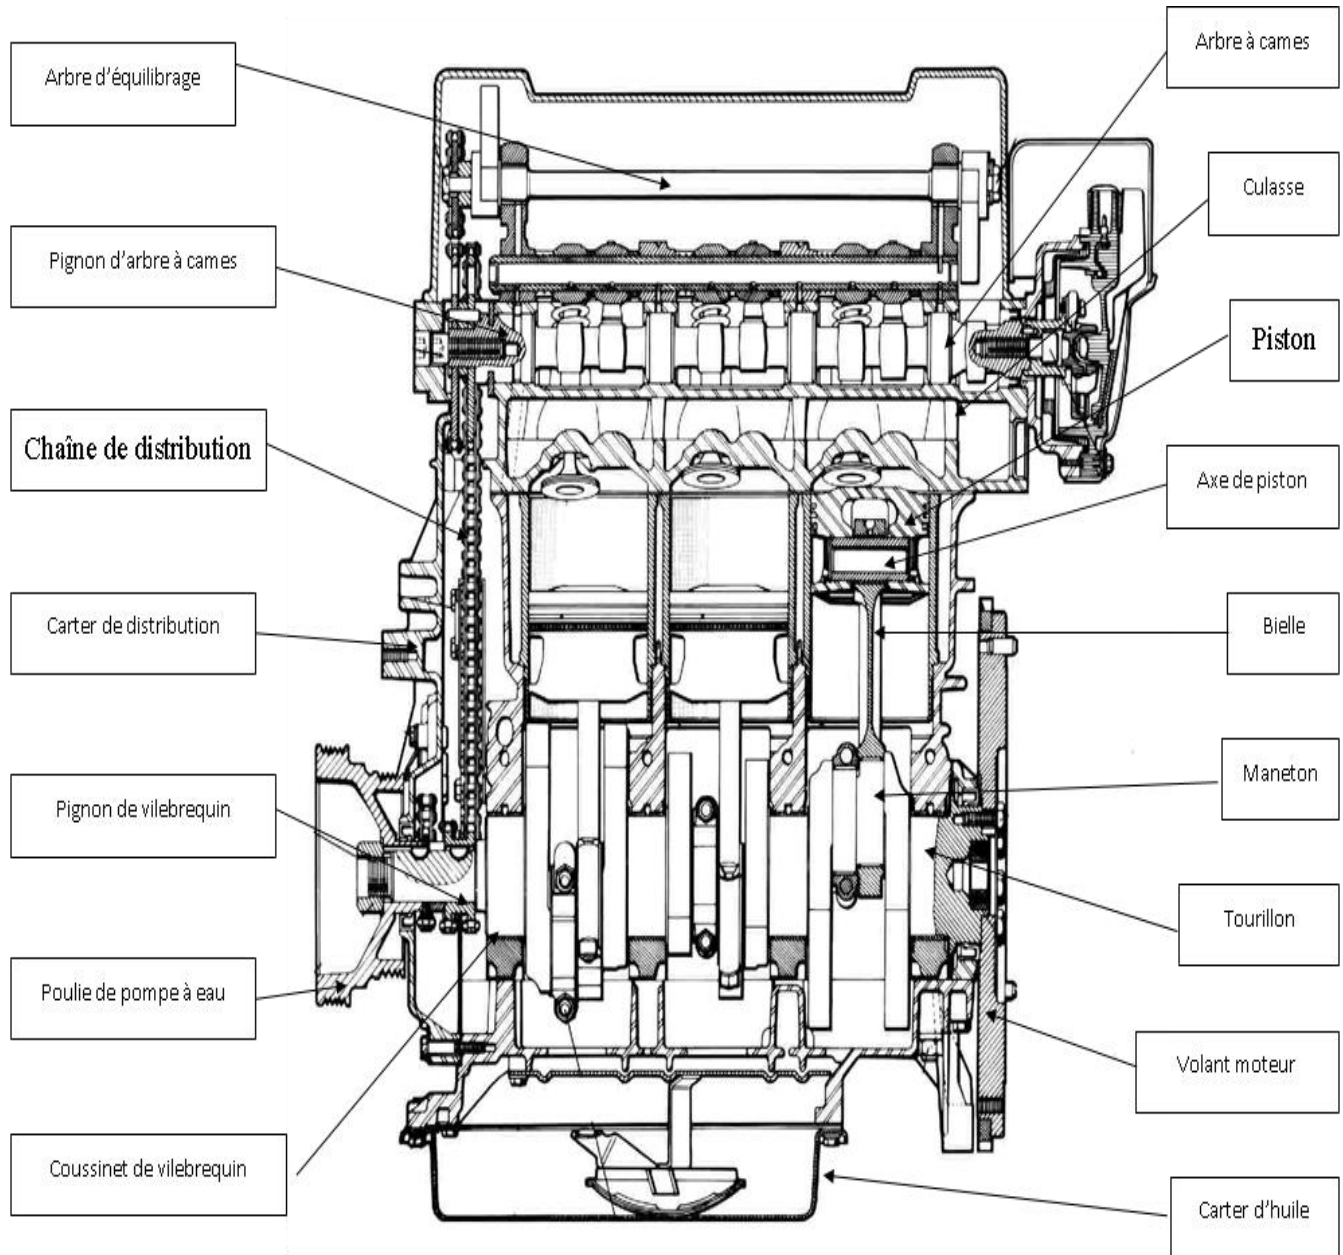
Schéma d'ensemble d'un moteur thermique [3].
